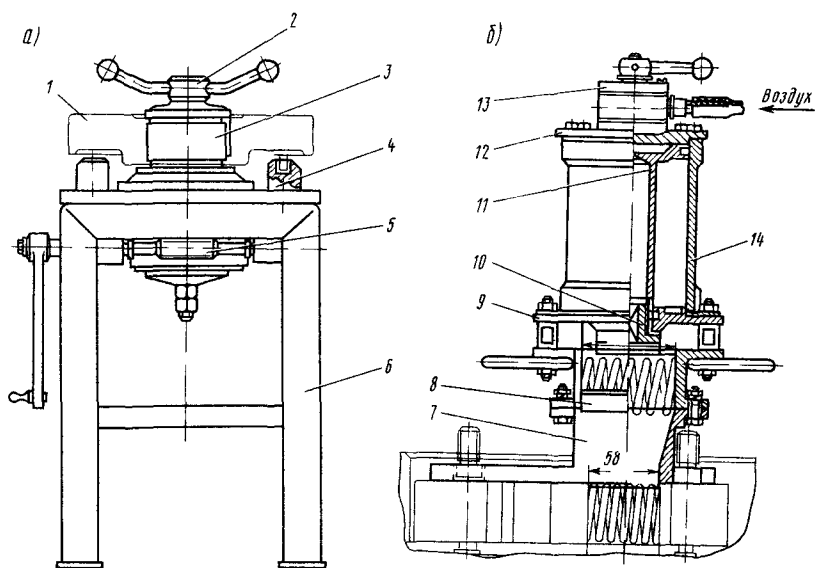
Стенд для сборки и разборки эластичного привода воздухо-
